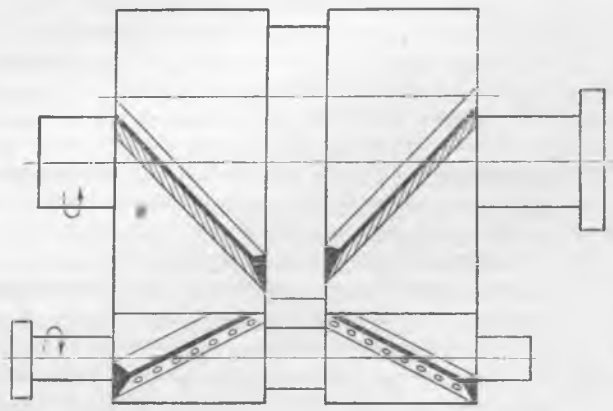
Шабровка изношенной стороны зубьев шестерни по исправленным зубьям колеса.
